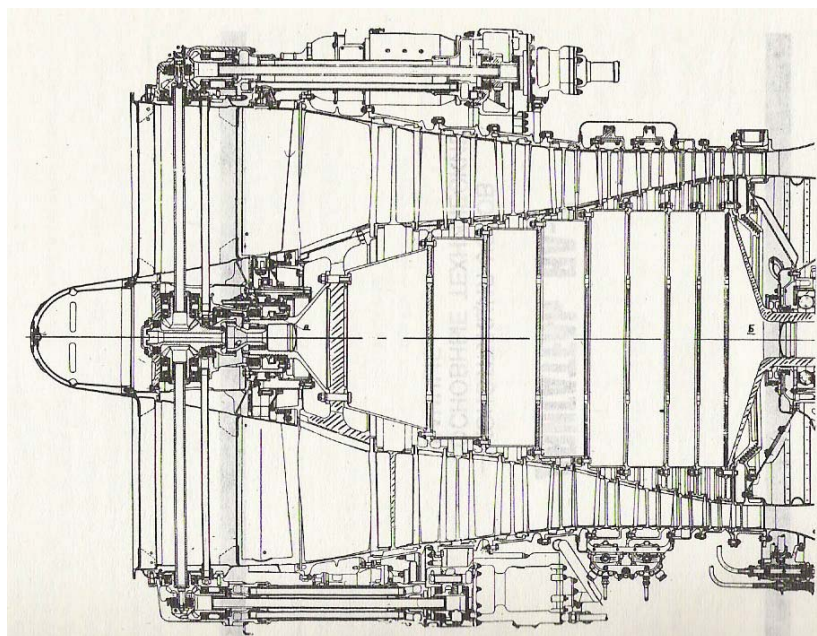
Разрез осевого компрессора турбореактивного двигателя ВД-7 с проточной частью комбинированного типа
